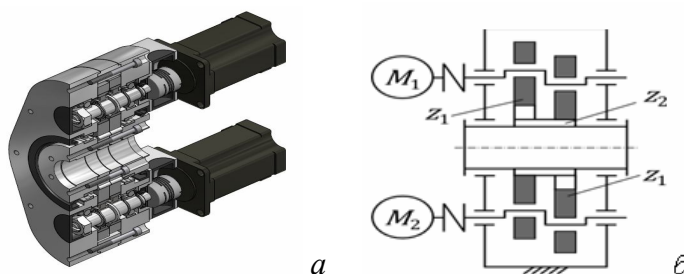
Конструкция (а) планетарно-цевочного мотор-редуктора с полым выходным валом, предлагаемая авторами и его кинематическая схема (б)
